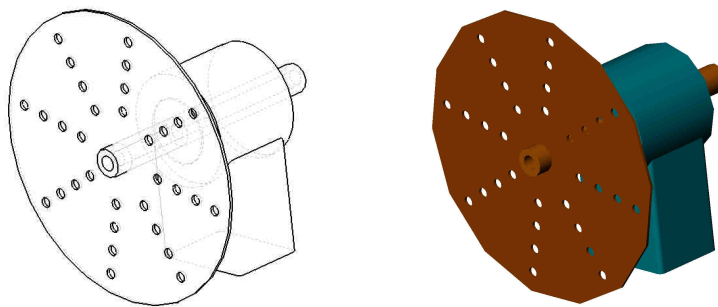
Diseño del plato perforado soporte del molde y del soporte de cojinetes de la máquina de rotomoldeo.
